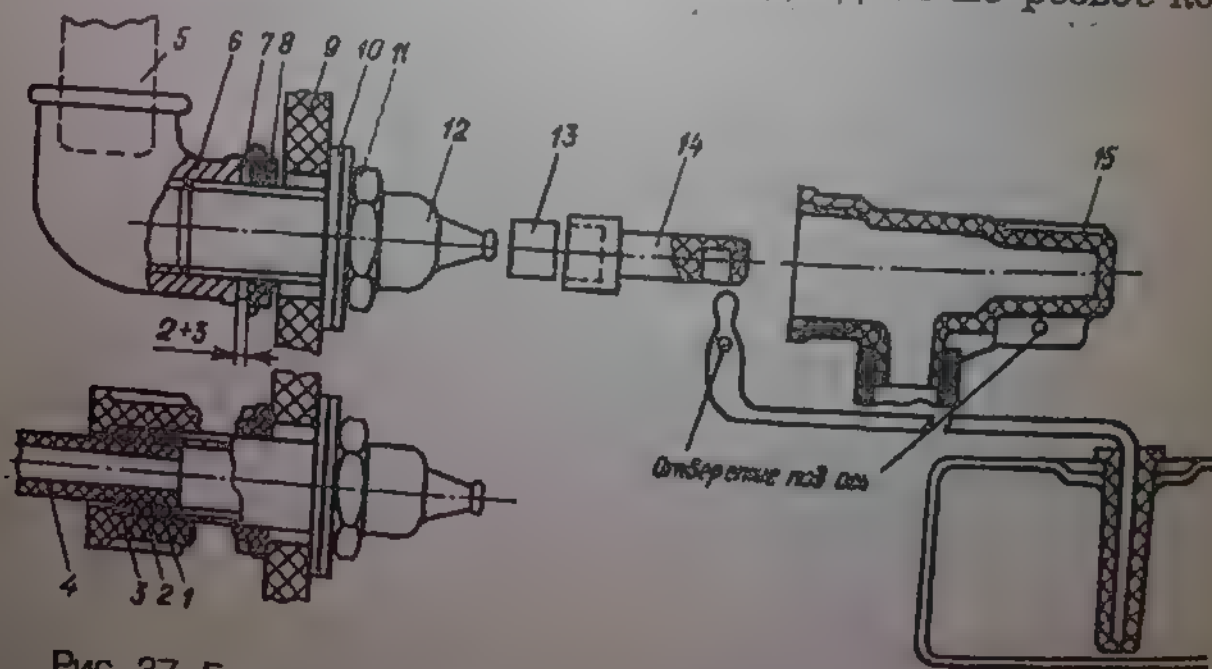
Горизонтальный пластмассовый поплавковый клапан:
